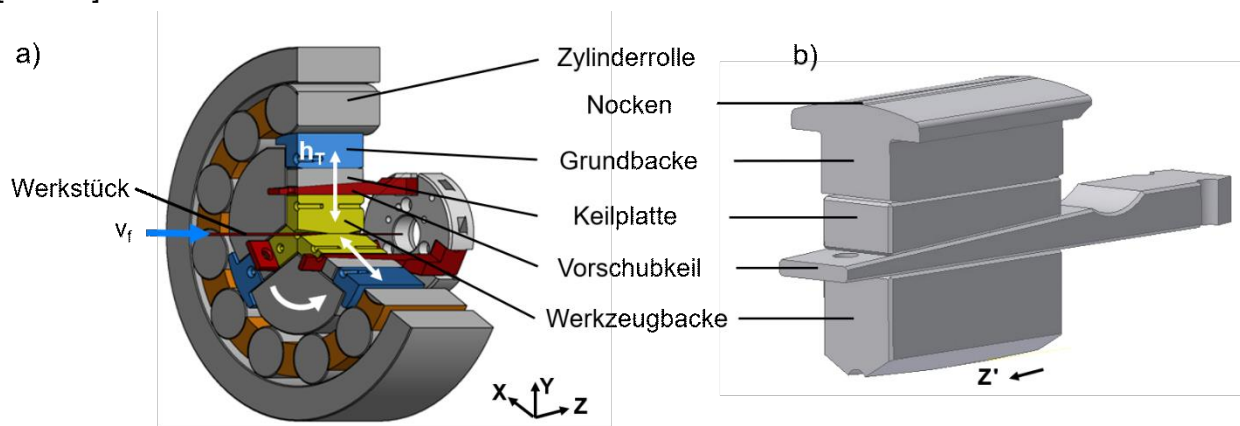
Rundkneten (Innenläufer): a) Knetkopf, Werkzeuge, Kinematik; b) Werkzeugsäule.
